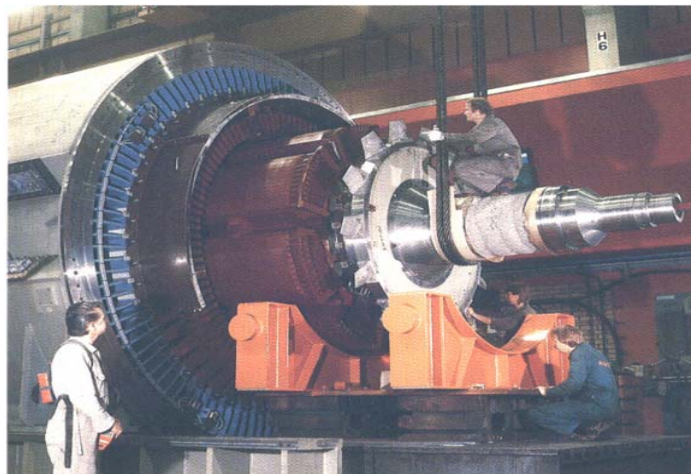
rotor d'une machine synchrone à pôles saillants [10]
